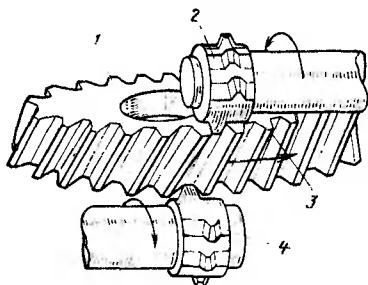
Схема обработки фасок червячными фрезами-улитками:
